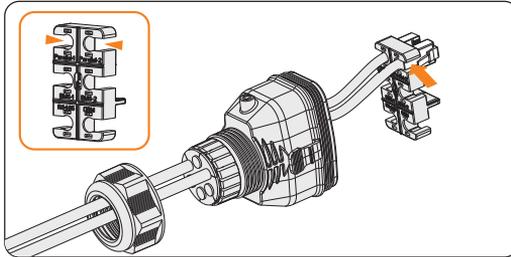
Kabel an der Kabelbefestigung anbringen
